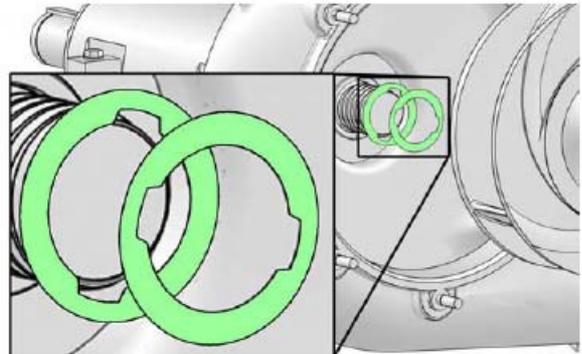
Instalação na junta entre luva e rotor
